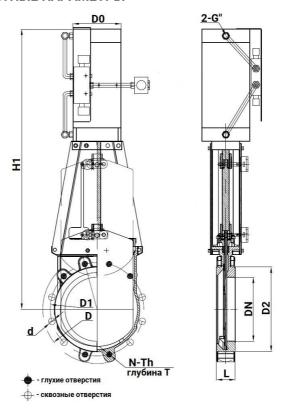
Размеры задвижки в сборе с пневмоцилиндром
